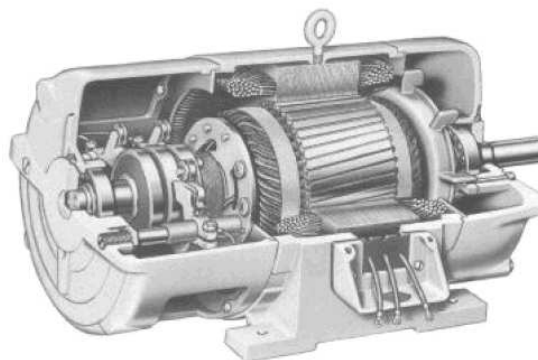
Máquina de inducción de rotor bobinado con anillos deslizantes
